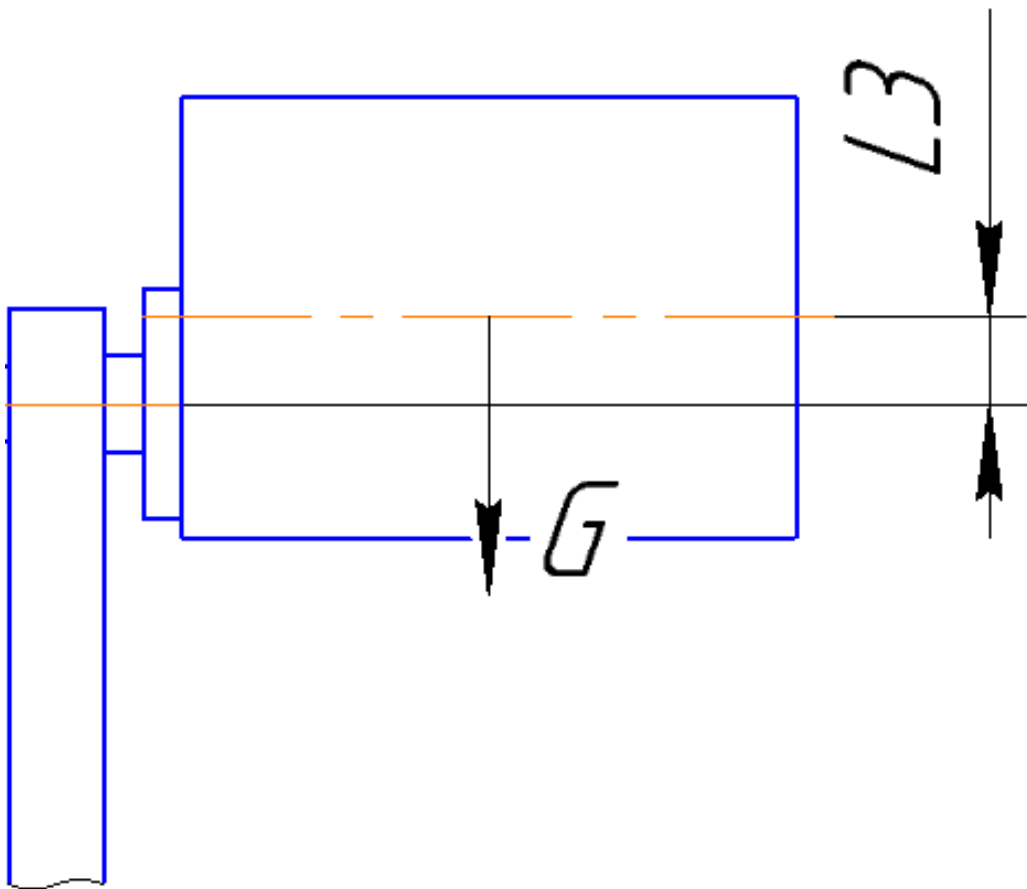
Схема несовпадения осей вала и центра масс двигателя
